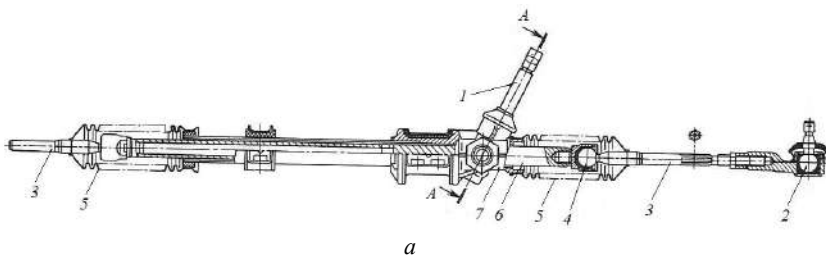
Рейковий рульовий механізм з установкою вала-шестерні:
